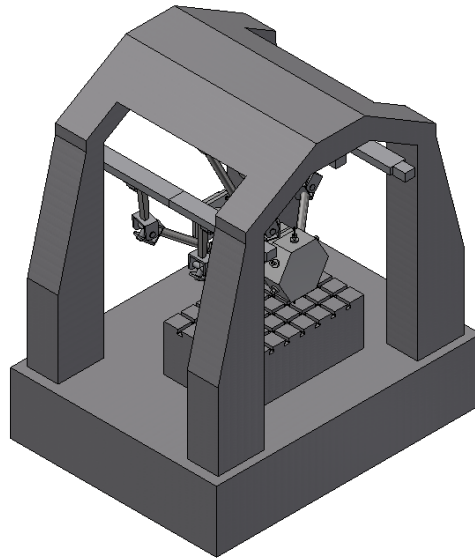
Общий вид компоновки резьбонарезного станка с комбинированным МПС с шестью степенями свободы
